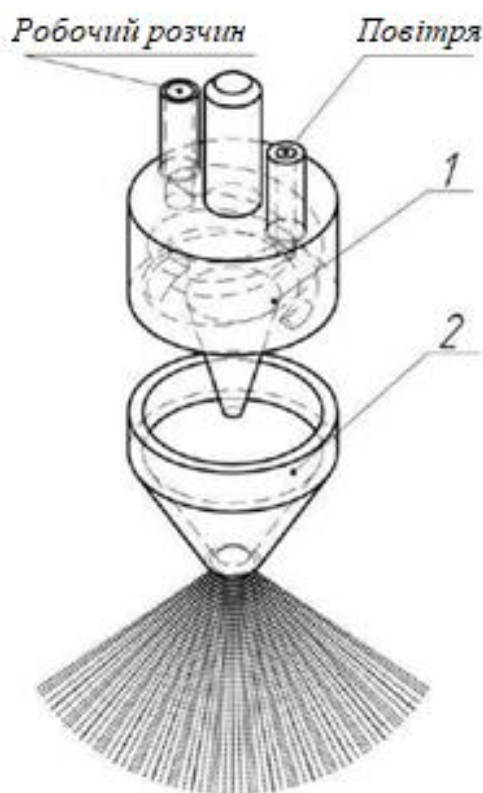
Розпилювач: 1 – корпус; 2 – сопло
